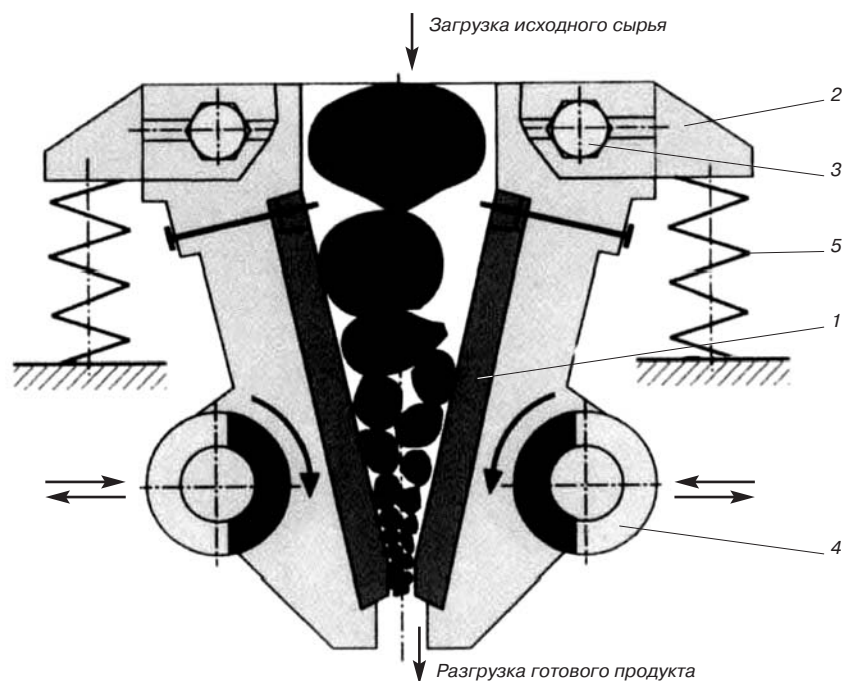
Конструктивная схема виброщелевой дробилки ВЩД: 1 – дробящая щека; 2 – корпус; 3 – торсион; 4 – вибровозбудитель; 5 – пружина
